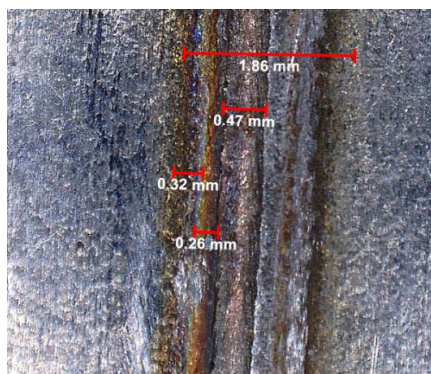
Material base de soldadura HF 100X, ataque vilella
